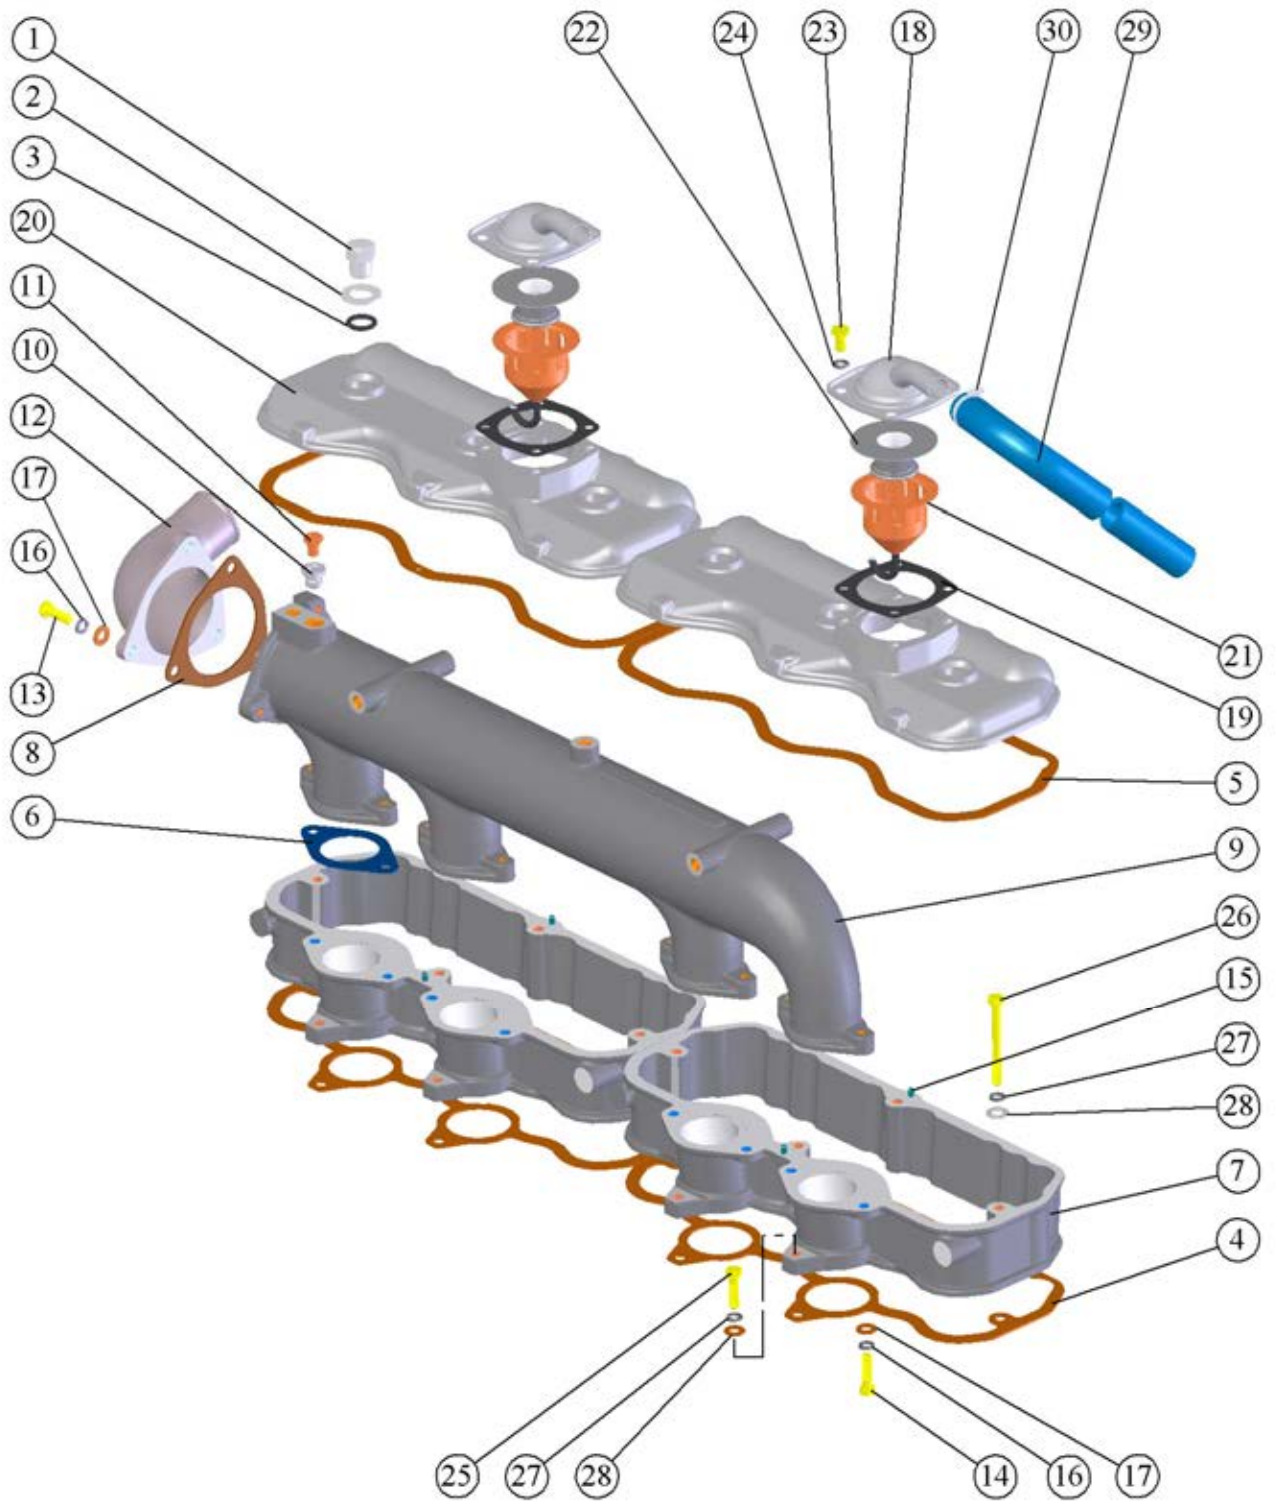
Крышки головок цилиндров, коллектор и сапуны.
